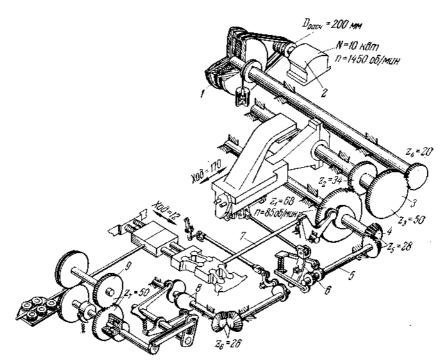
Кинематическая схема двухударного автомата с разъемной матрицей
